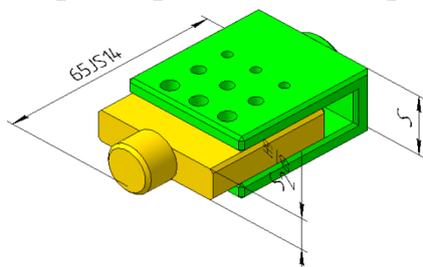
Общий вид приспособления для проведения испытаний заклепочных соединений
